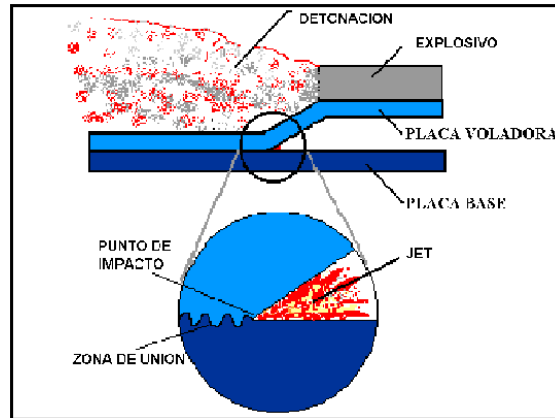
Arreglo para la Soldadura por Explosión
